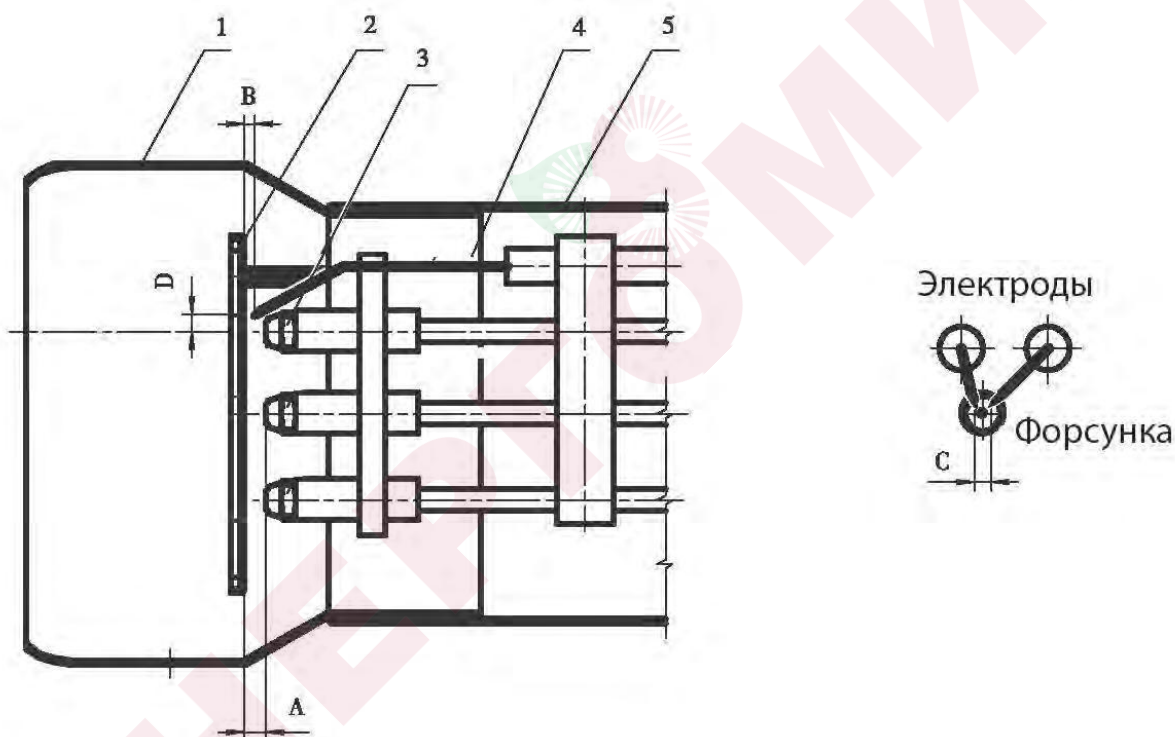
Горелка NORTEC WB 650ST с 6-ю форсунками
